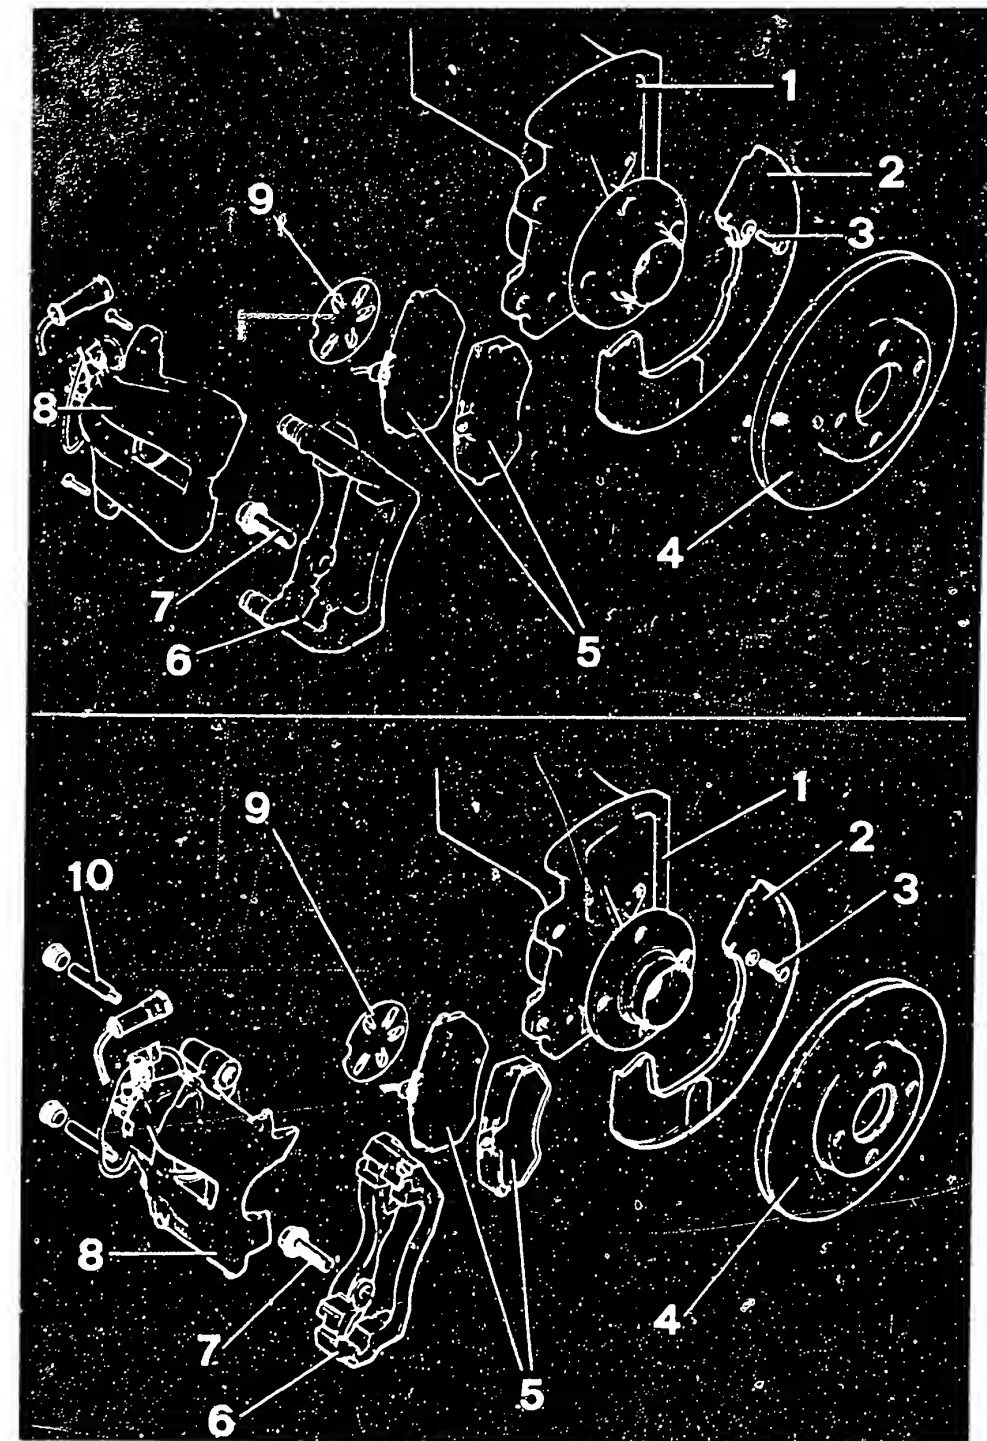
Scheibenbremse vorn mit Girling- (oben) oder ATE- (unten) Bremsattel: 1 Radlagergehäuse - 2 Abdeckblech - 3 Schraube - 4 Bremsscheibe - 5 Bremsklötze - 6 Bremsträger - 7 Befestigungsschraube - 8 Bremsattelgehäuse - 9 Wärmeschutzblech - 10 Führungsbolzen.
